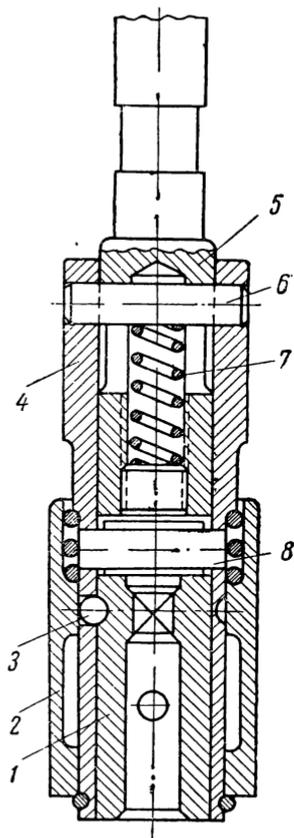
Быстросменный патрон для метчиков (с компенсатором)
